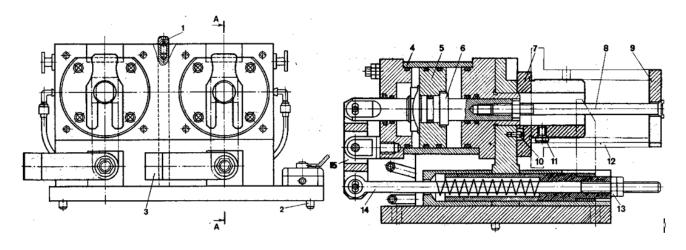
Приспособление двухместное специализированное для установки заготовок типа фланец Система применяется также при групповой обработке заготовок.
